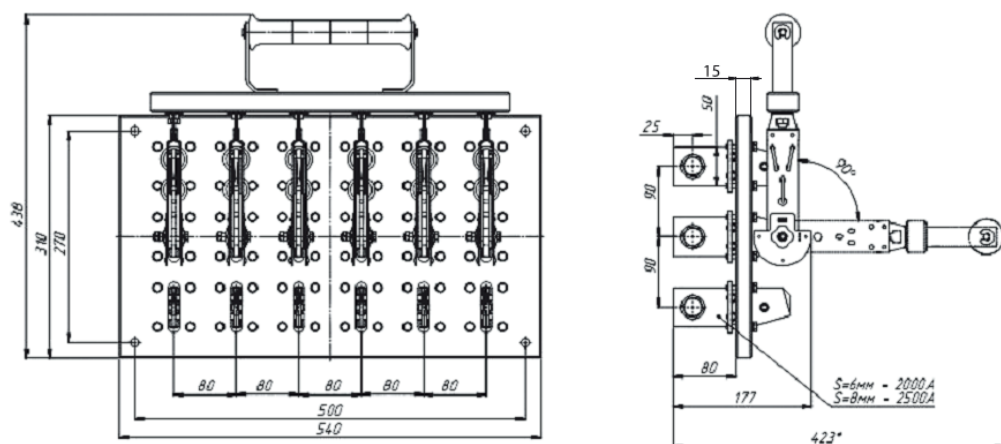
Разъединитель РЕ19 с центральным рычагом для управления штангой
